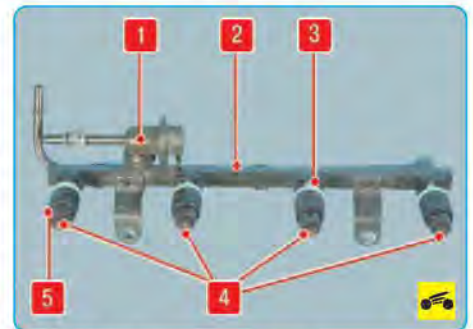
Топливная рампа: 1 – регулятор давления топлива; 2 – рампа; 3 – фиксатор форсунки; 4 – форсунки; 5 – уплотнительное кольцо форсунки
